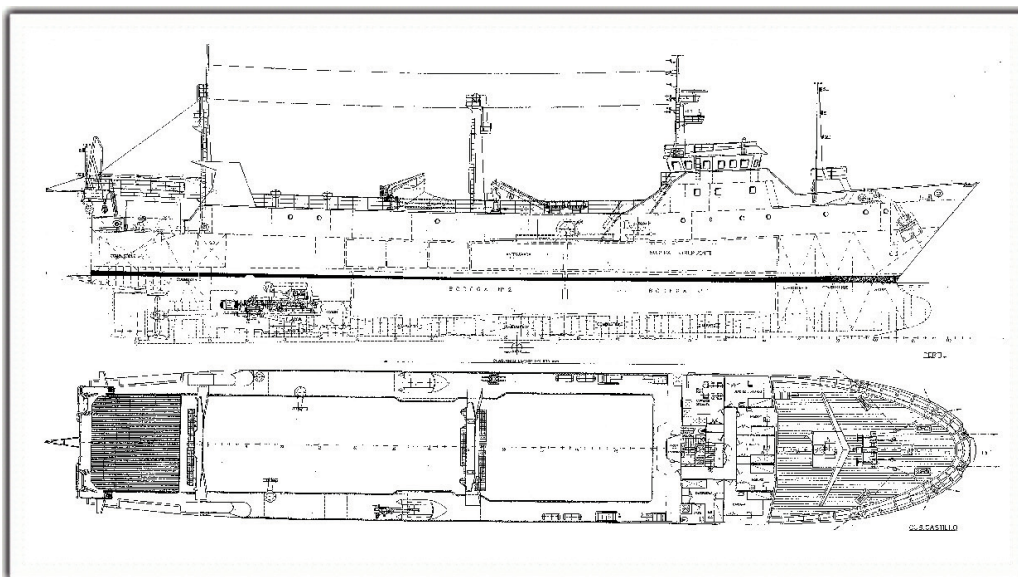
Alzado y planta de la cubierta principal del B/P MANUEL ÁNGEL NORES.
